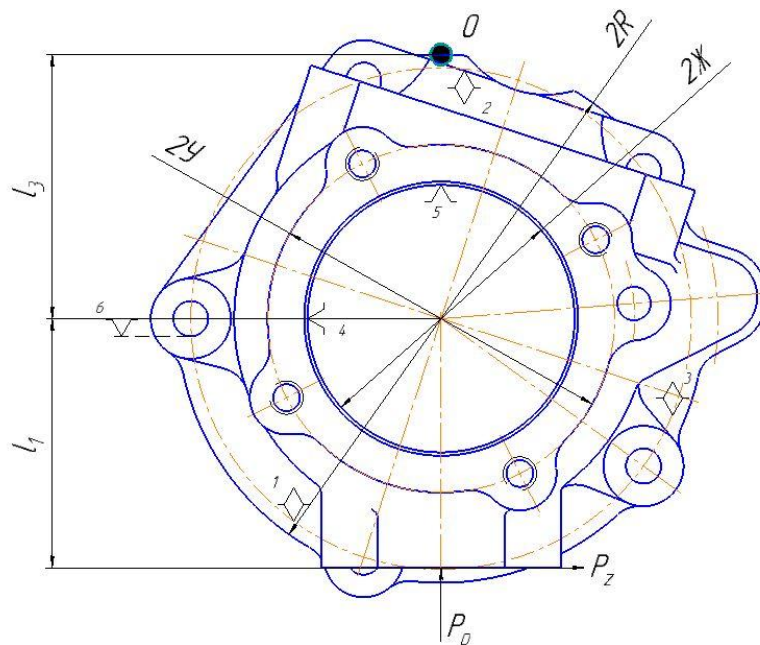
Схема обработки при условии опрокидывания заготовки
